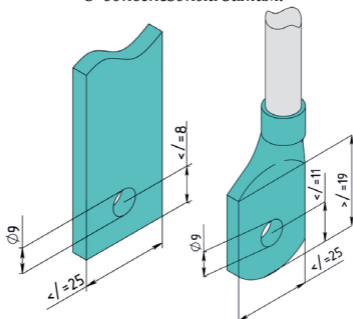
Форма и размеры присоединяемой шины максимального сечения выключателя
